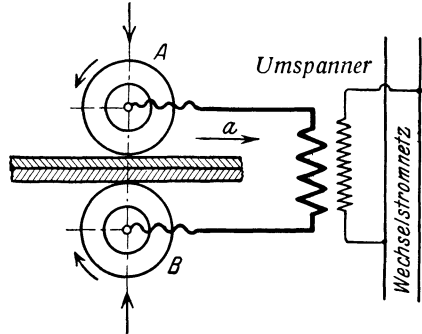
Grundform der elektrischen Nahtschweißung.
